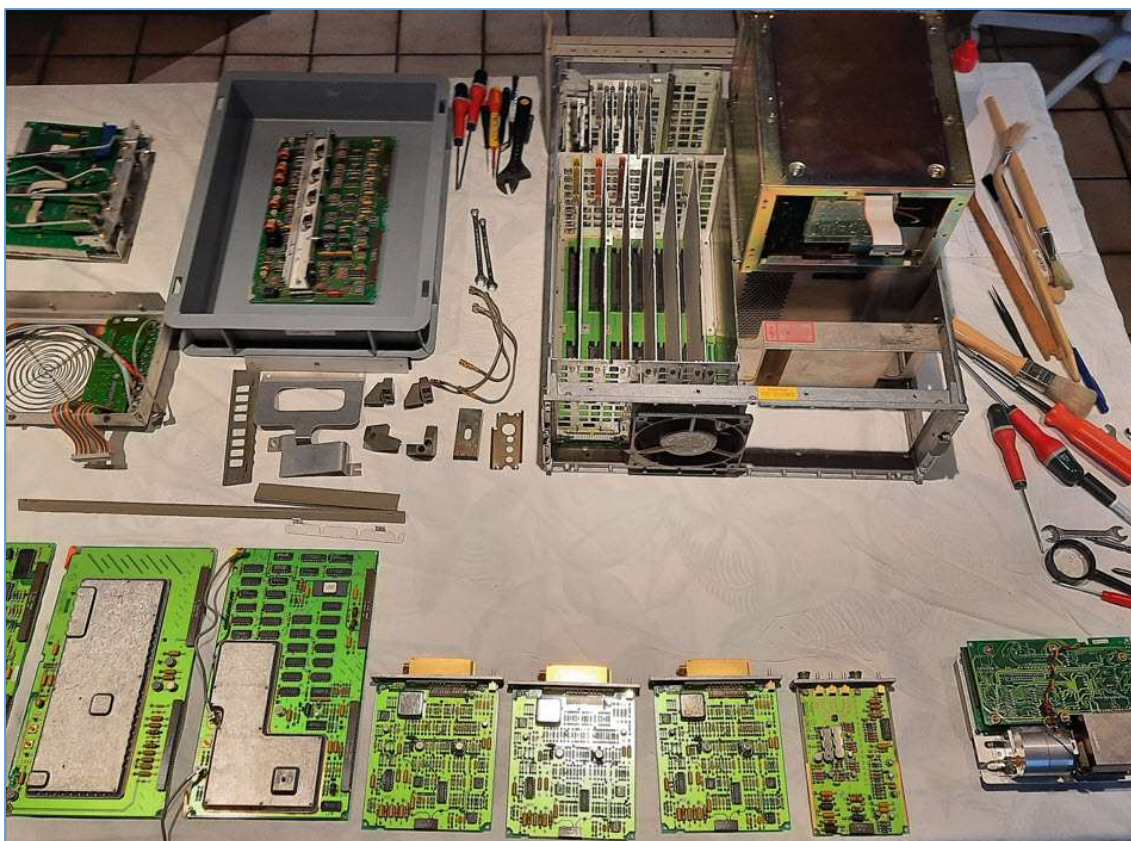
Ensemble des cartes, sous-ensembles et rack du VNA HP 8753C. Photo : ON4IJ.
